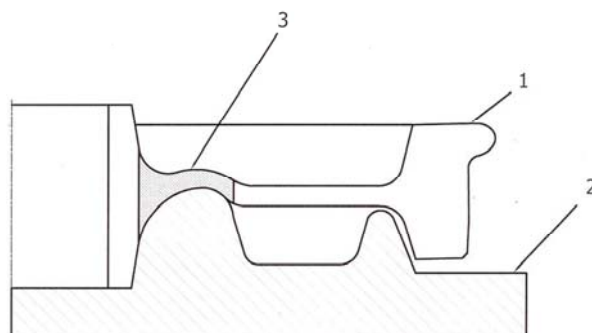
Схема самоцентрировки колеса на прессе 35 МН:
